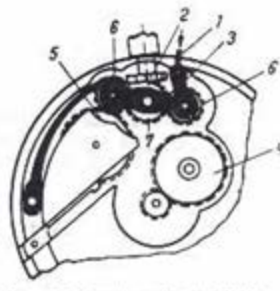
Mecanismul remotor cu pod basculant și buton de apăsare.
